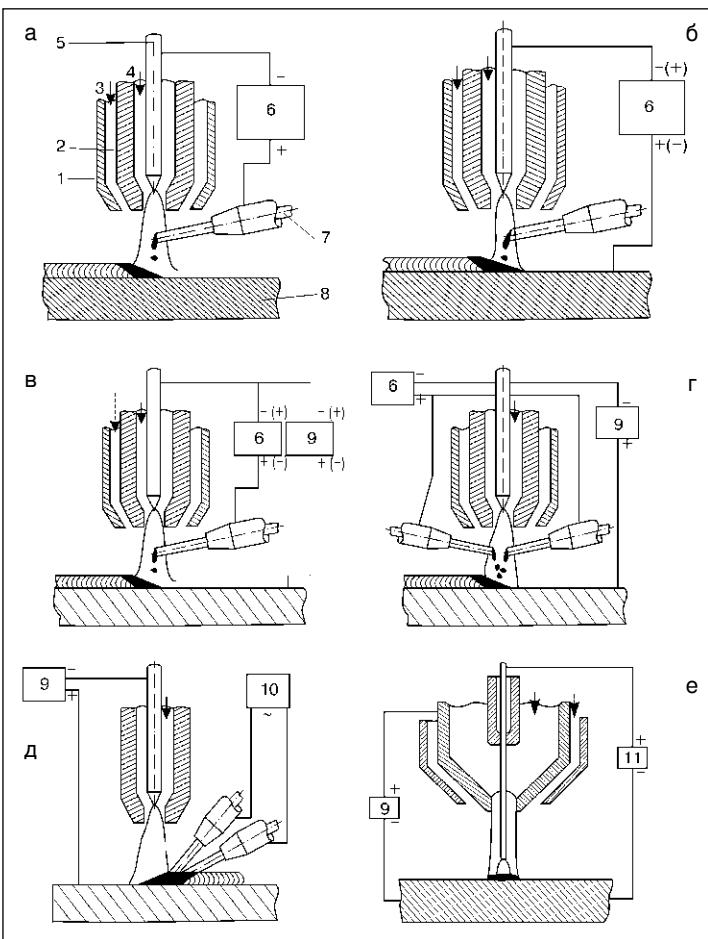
Схемы плазменной наплавки: а — плазменной струей с токоведущей присадочной проволокой; б — плазменной дугой с нейтральной присадочной проволокой; в — комбинированная наплавка плазменной дугой с одной токоведущей присадочной проволокой; г — комбинированная плазменной дугой с двумя присадочными проволоками; д — горячая проволокой; е — плавящимся электродом (1 — защитное сопло; 2 — плазмообразующее сопло; 3 — защитный газ; 4 — плазмообразующий газ; 5 — электрод; 6 — источник питания косвенной дуги; 7 — присадочная проволока; 8 — основной металл; 9 — источник питания дуги прямого действия; 10 — трансформатор; 11 — источник питания дуги плавящегося электрода)
